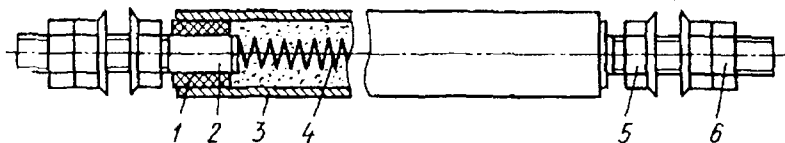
Трубчатый электронагреватель: 1 – изолятор; 2 – выводной стержень; 3 – корпус; 4 – нихромовая спираль; 5, 6 – клеммные гайки.
